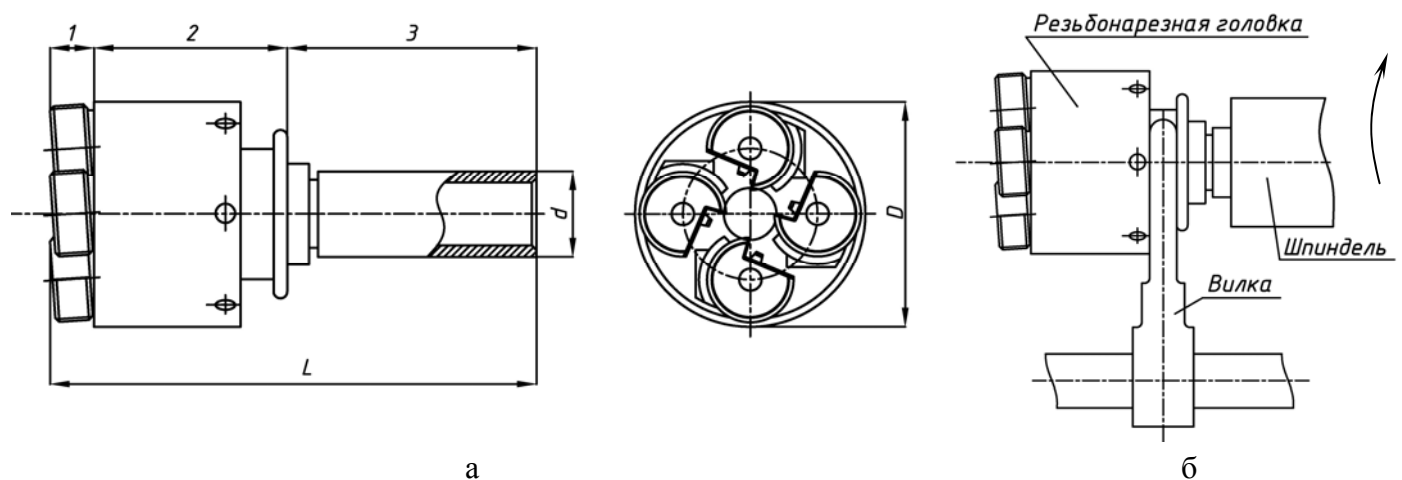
Вращающаяся резьбонарезная головка для наружной резьбы.
